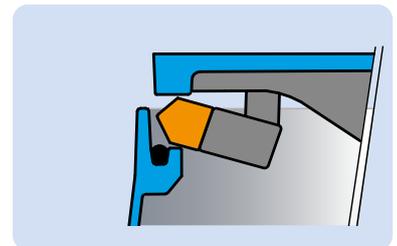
Federstab verbogen: Position zu nah an Deckelunterseite und zu weit außen, Deckel lässt sich nicht schliessen
